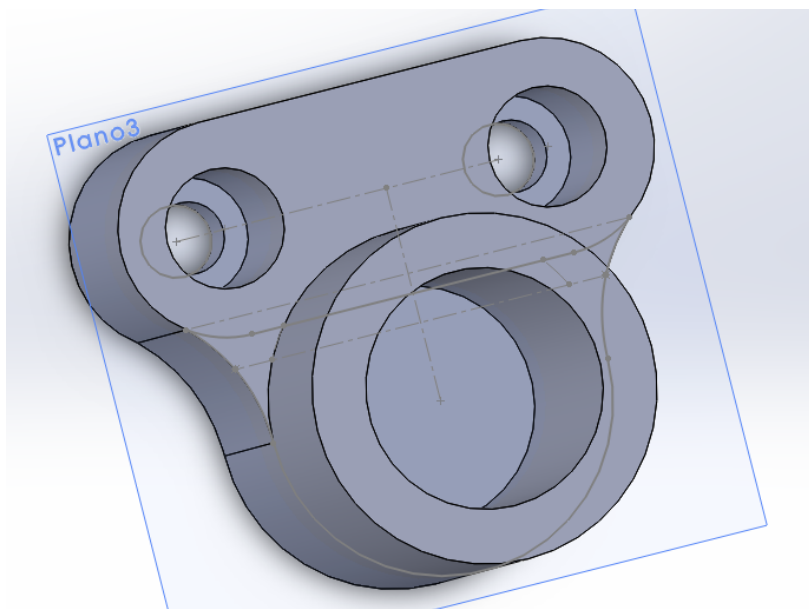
Diseño de la base de la torrecilla de la antena GPS. *Fuente: Autor.
